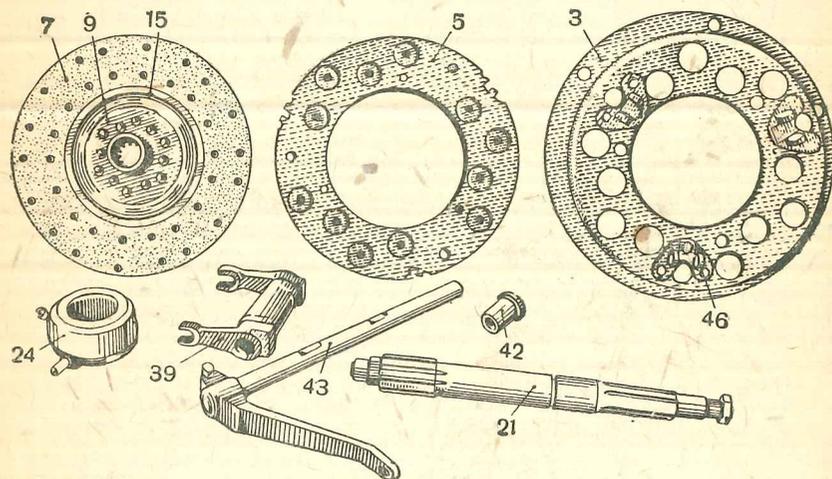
Детали кожуха, диска и валика муфты сцепления.
